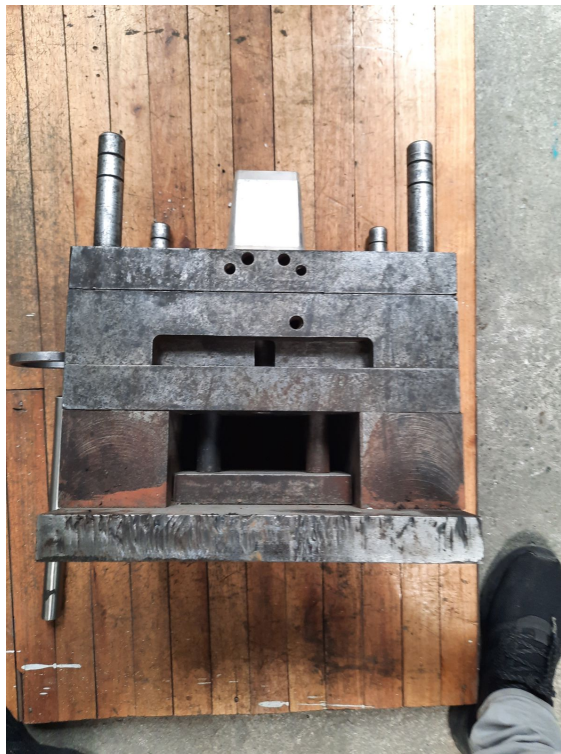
Molde antiguo de la “Empresa Metal Mecánica Galán”.
